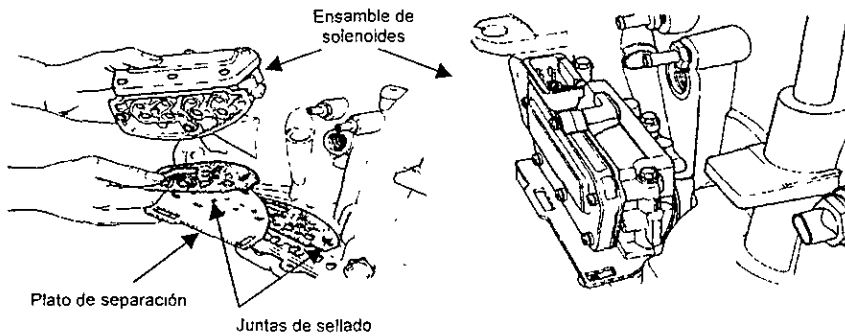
Ensamble del conjunto de solenoides en la carcasa (Cortesía Chrysler)
